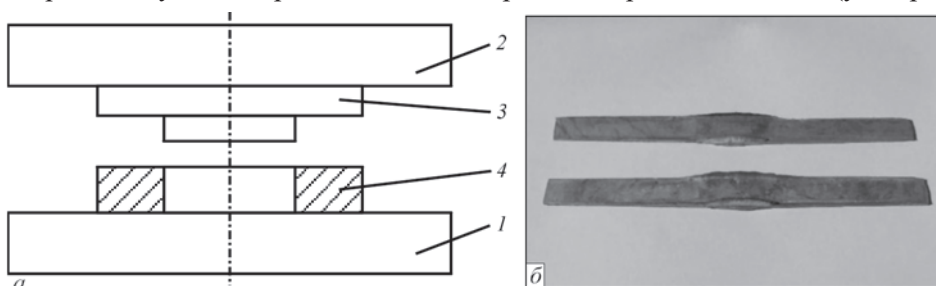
Схематичне зображення оснащення для проведення дифузійного зварювання у вакуумі з використанням формуючих матриць: 1, 2 – фланці; 3 – пуансон; 4 – матриця (а), вигляд зразків після зварювання (б)
